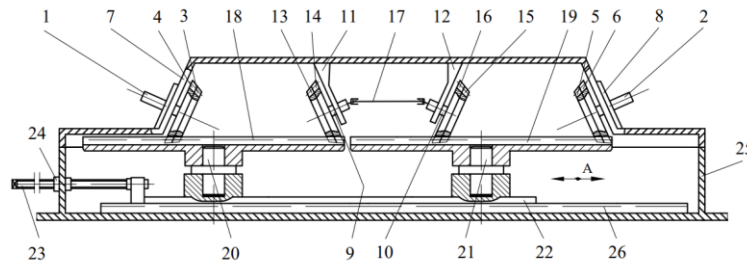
Четырехступенчатый вариатор с коническими зубчатыми колесами
